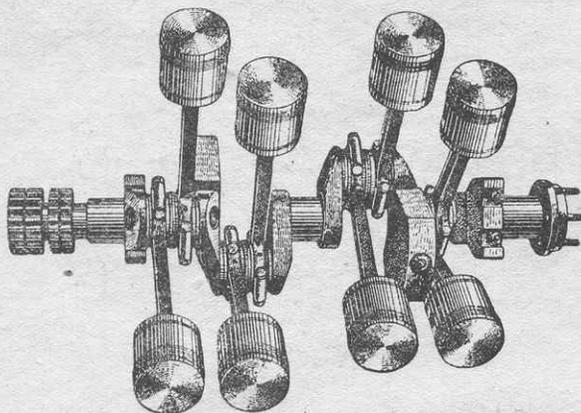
Компенсированный уравновешенный коленчатый вал восьмицилиндрового двигателя автомобиля Кадилак, с шатунами и поршнями.
